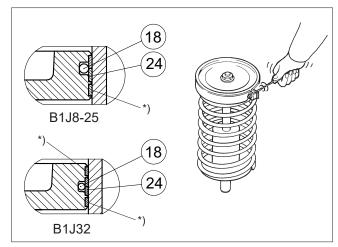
Serrage des joints du piston à l'aide d'un anneau de serrage
